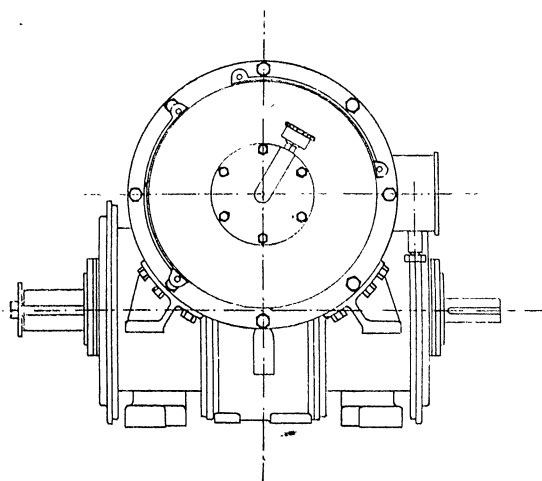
Rudergeschirr mit unmittelbar angebauter Rudermaschine, Schneckenvorgelege und Druckluftumkupplung
